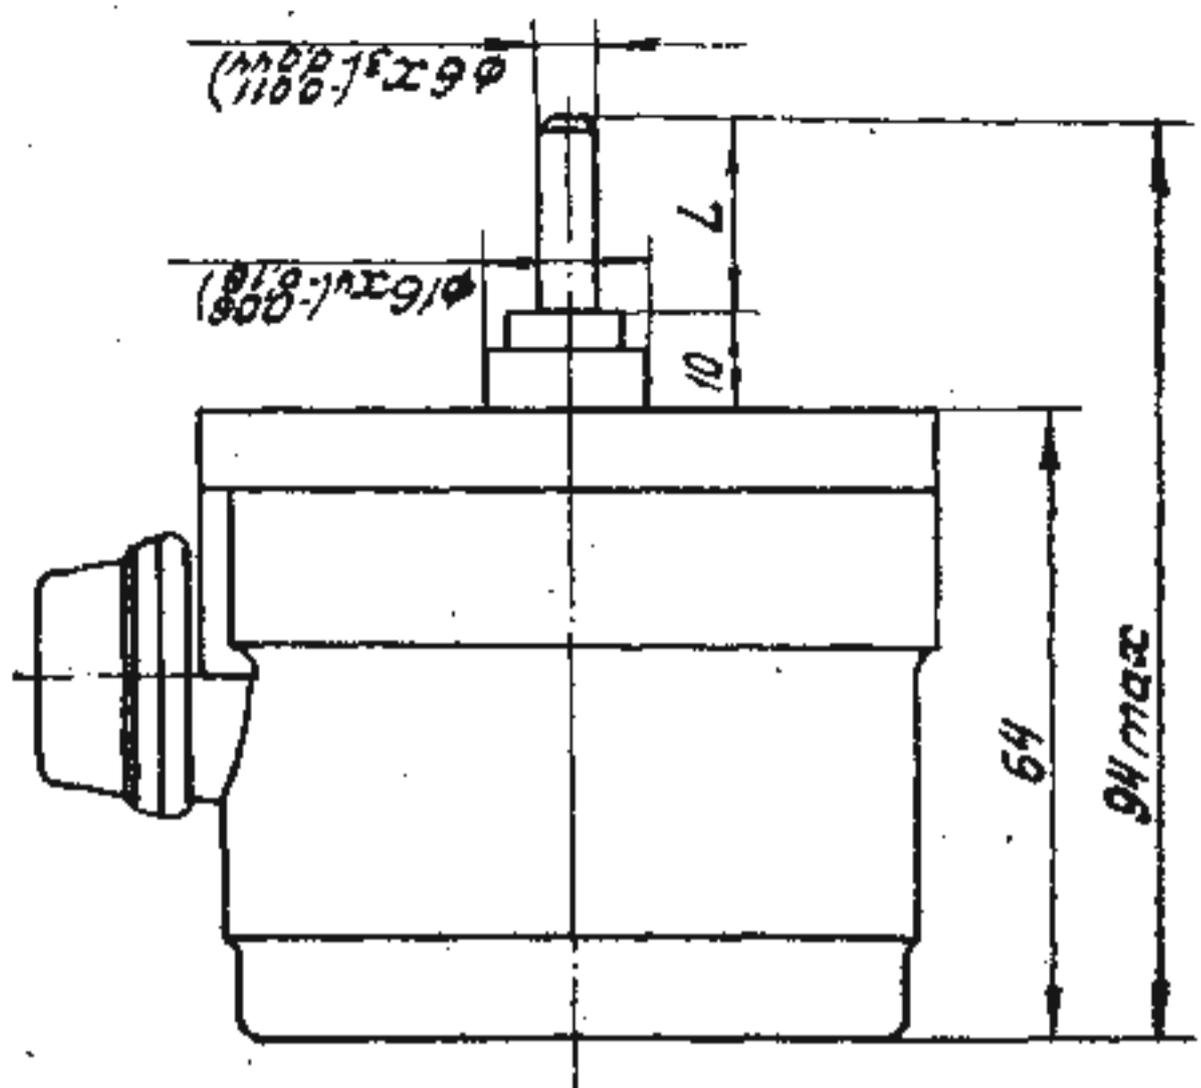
Габаритные и присоединительные размеры электродвигателя:
